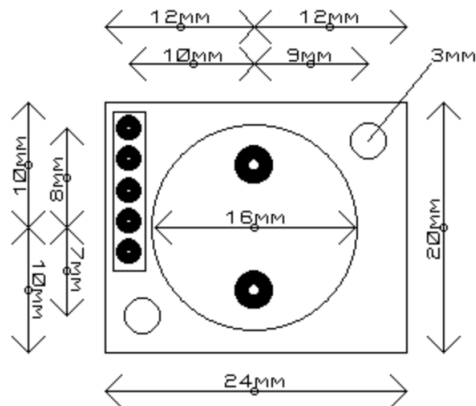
Dimensiones físicas del ultrasónico Devantech SRF02 [27].
